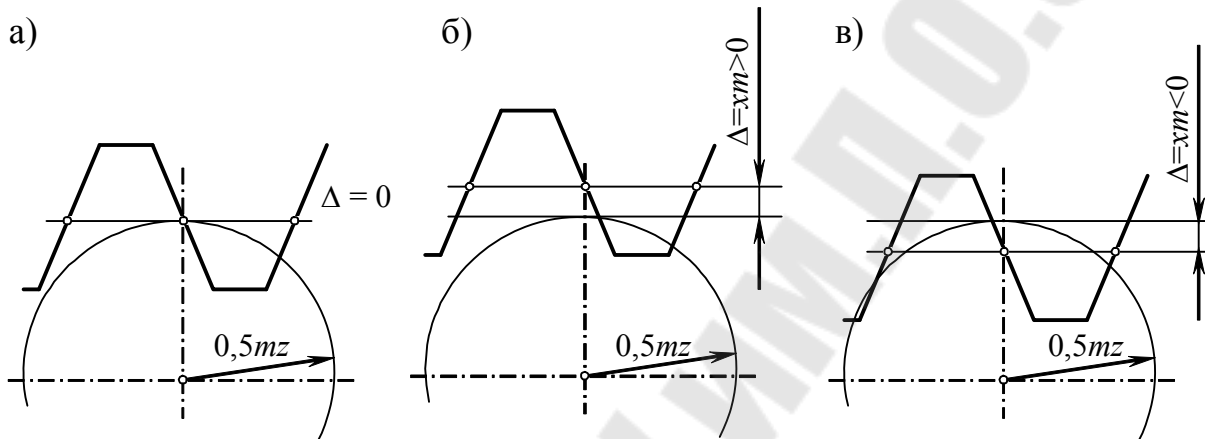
Расположение инструментальной рейки и заготовки зубчатого колеса при изготовлении нулевого (а), положительного (б) и отрицательного (в) колеса
